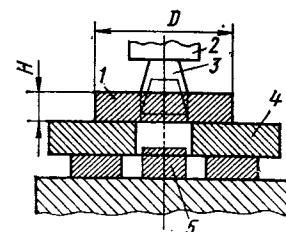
Прошивка на подкладном кольце: 1 — заготовка; 2 — боек; 3 — прошивень; 4 — кольцо; 5 — отход металла
